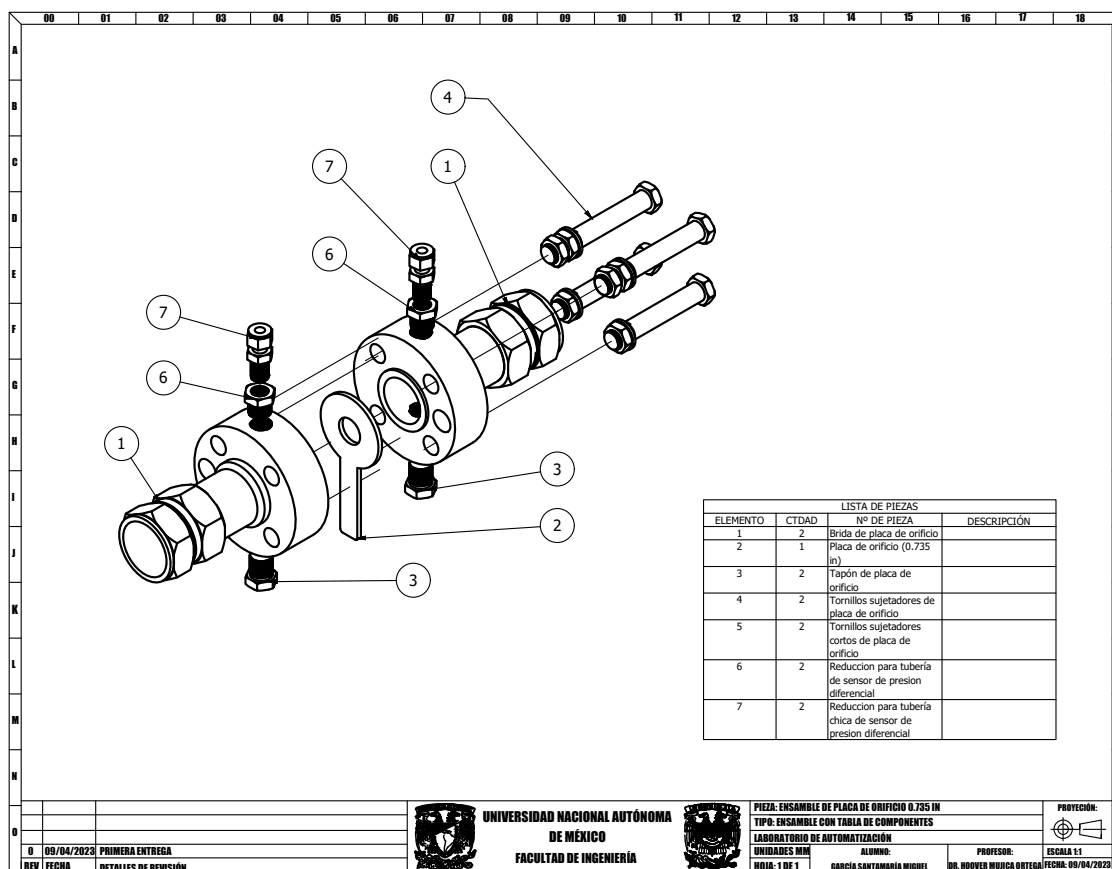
Ensamble explosionado y tabla de componentes de placa de orificio
